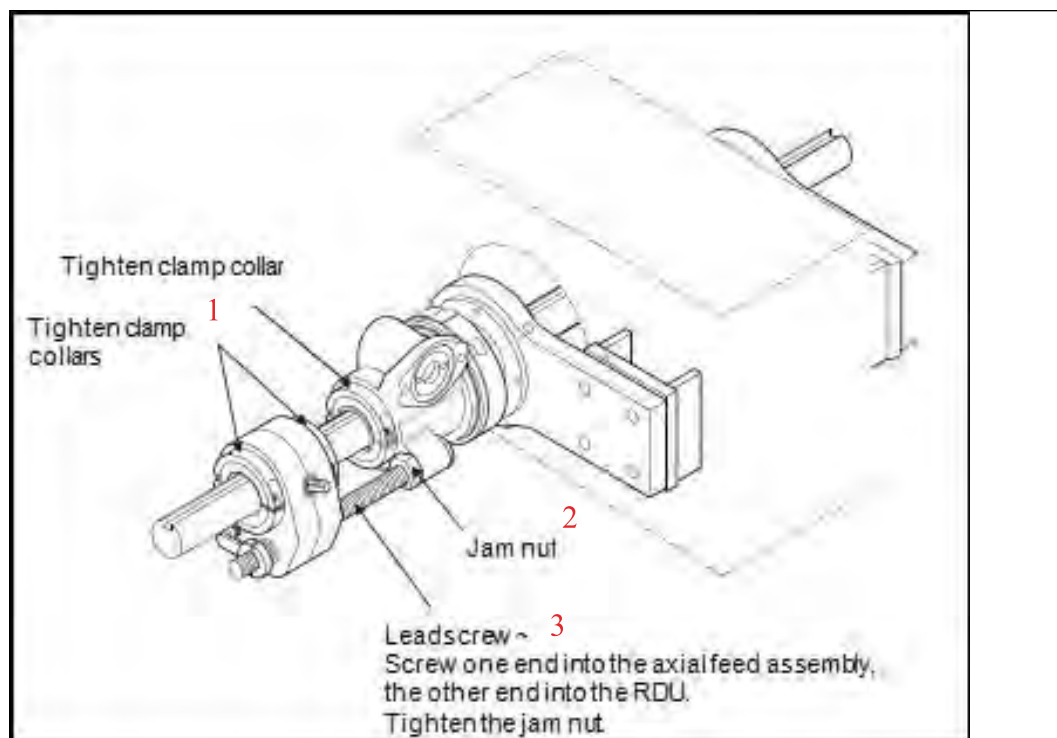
COLLIERS DE SERRAGE SUR L'AFU
